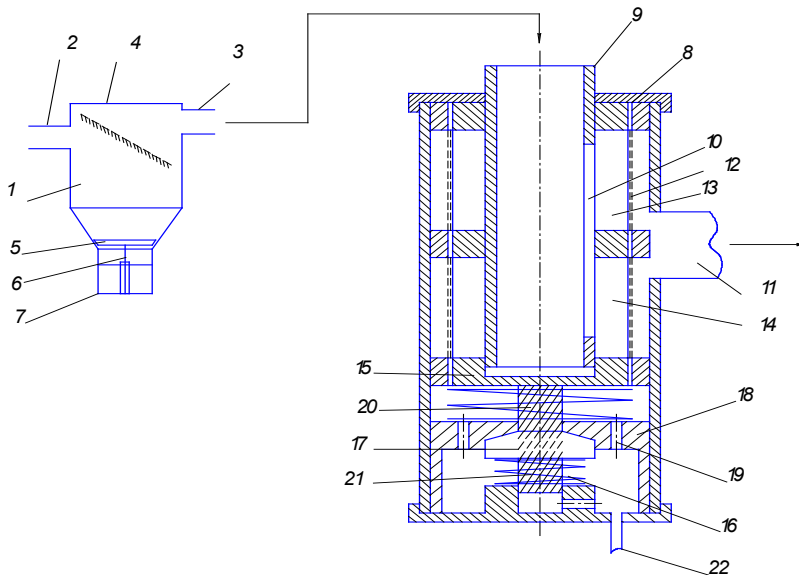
Схема молочного фільтра: 1-приймач молока; 2-вхідний патрубок; 3-вихідний патрубок; 4-фільтр грубої очистки; 5-конусна пробка; 6-шток; 7-відстійник; 8-корпус; 9-циліндрова камера; 10-бічна щілина; 11-вихідний патрубок; 12-фільтруючий елемент; 13-біличе колесо; 14-ребро бічне; 15-поршень; 16-хвостик; 17-гайка; 18-опорна втулка; 19-напрямні отвори; 20,21-пружини; 22-стік
